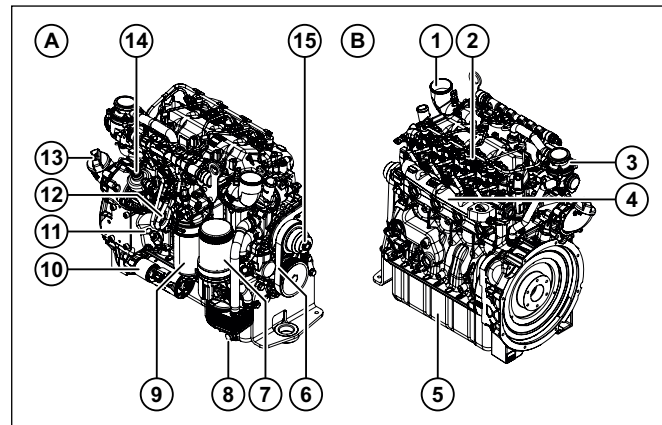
Dieselmotorbaugruppen (Hatz-Dieselmotor)
